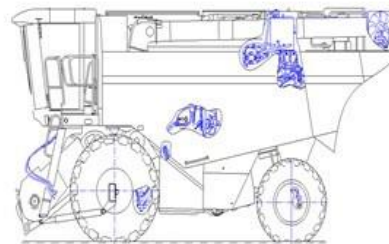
Сборочный чертеж гидросистемы комбайна
